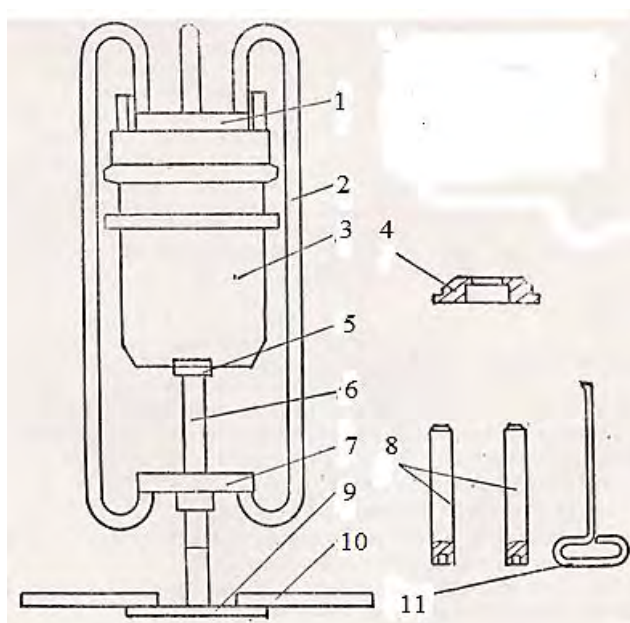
Приспособление для разборки и сборки тормозных камер КамАЗ: 1 – упор; 2 – скоба; 3 – тормозная камера КамАЗ; 4 – приставка; 5 – прижим; 6 – винт; 7 – гайка; 8 – оправка; 9 – основание; 10 – ручка; 11 – крючок
